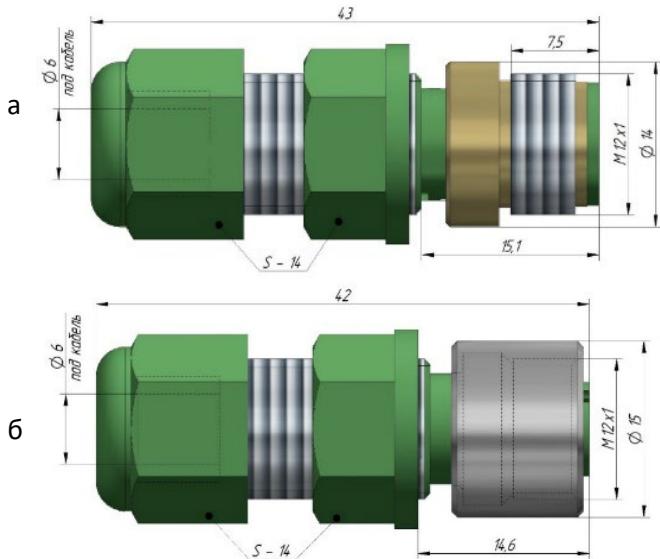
Внешний вид и габаритные размеры разборных кабельных разъемов:
